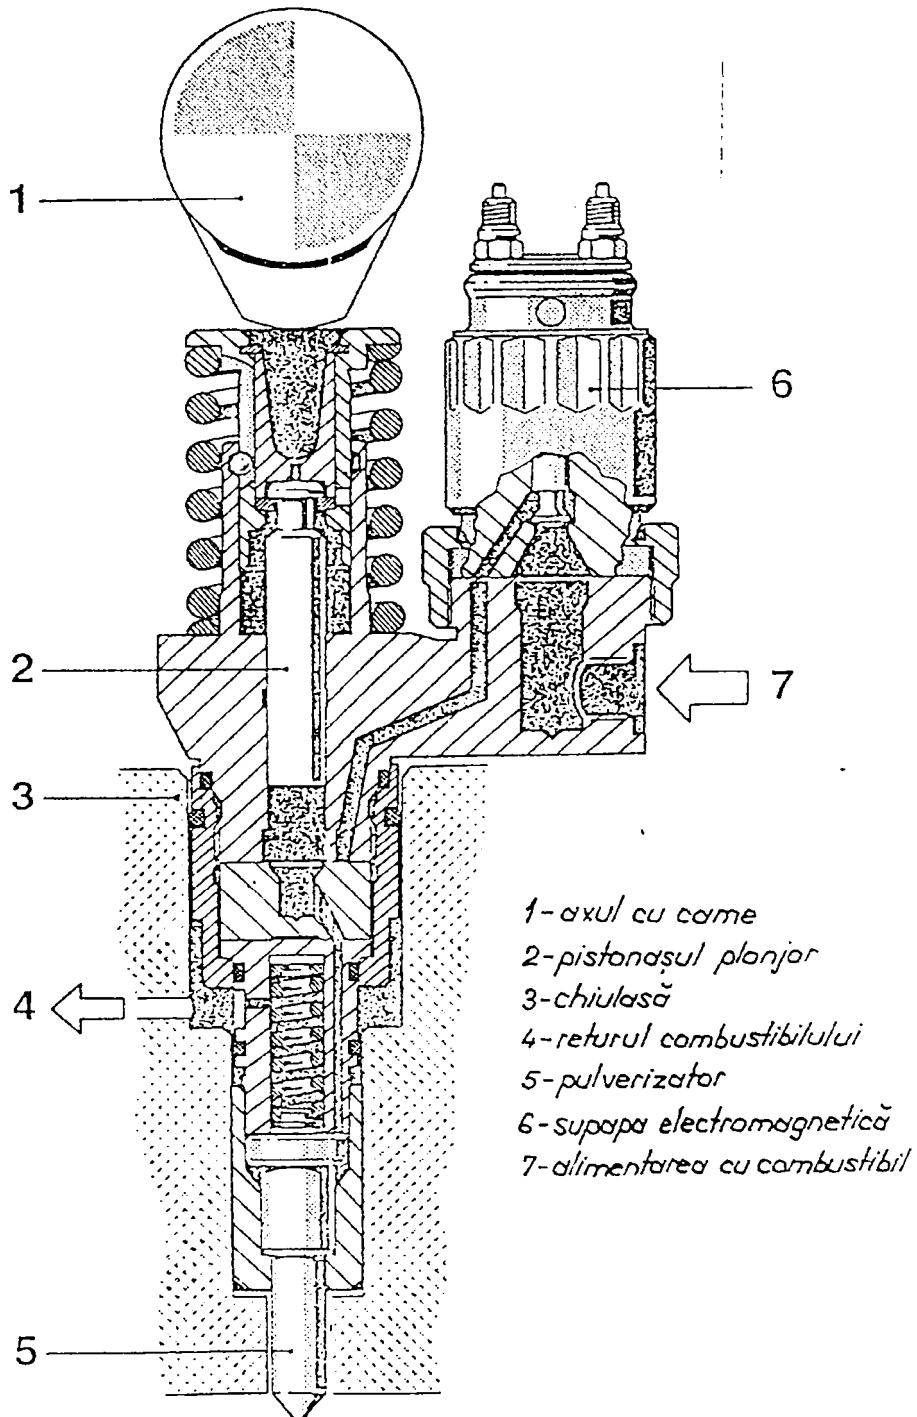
Secțiune prin ansamblul pompă - injector
